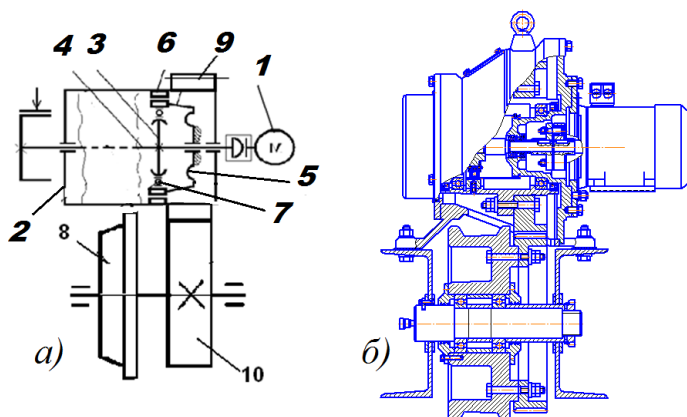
Механизм передвижения : а – схема; б- конструкция
